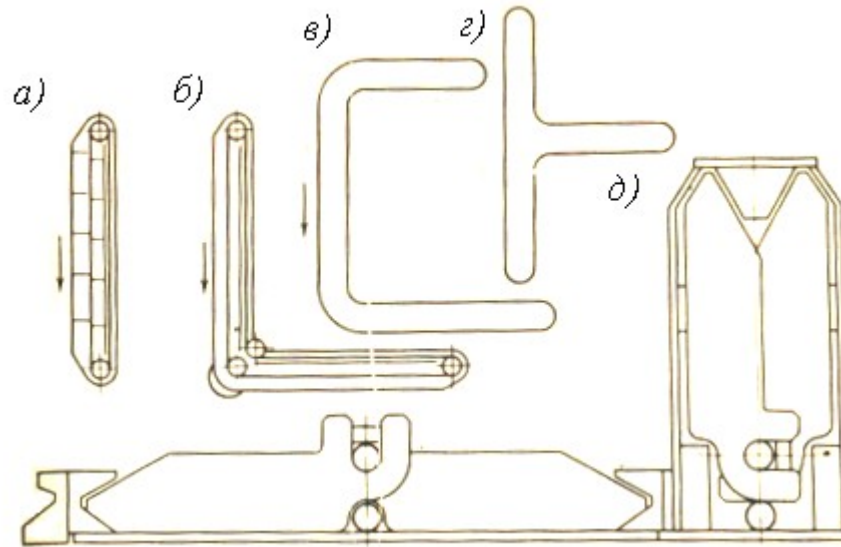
Скребокый конвейер с шарнирным закреплением складывающегося скребка:
